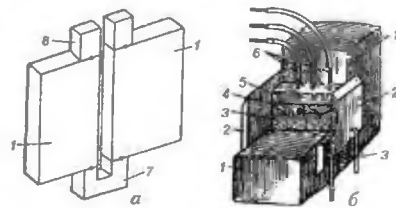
Електрошлакове зварювання: а — зображення під зварювання; б — схема процесу зварювання; 1 — зварні деталі; 2 — формуючі повзуни; 3 — зварний шов; 4 — шлакова ванна; 5 — шлакова ванна; 6 — електроди; 7 — з'єднана планка; 8 — виділена планка
